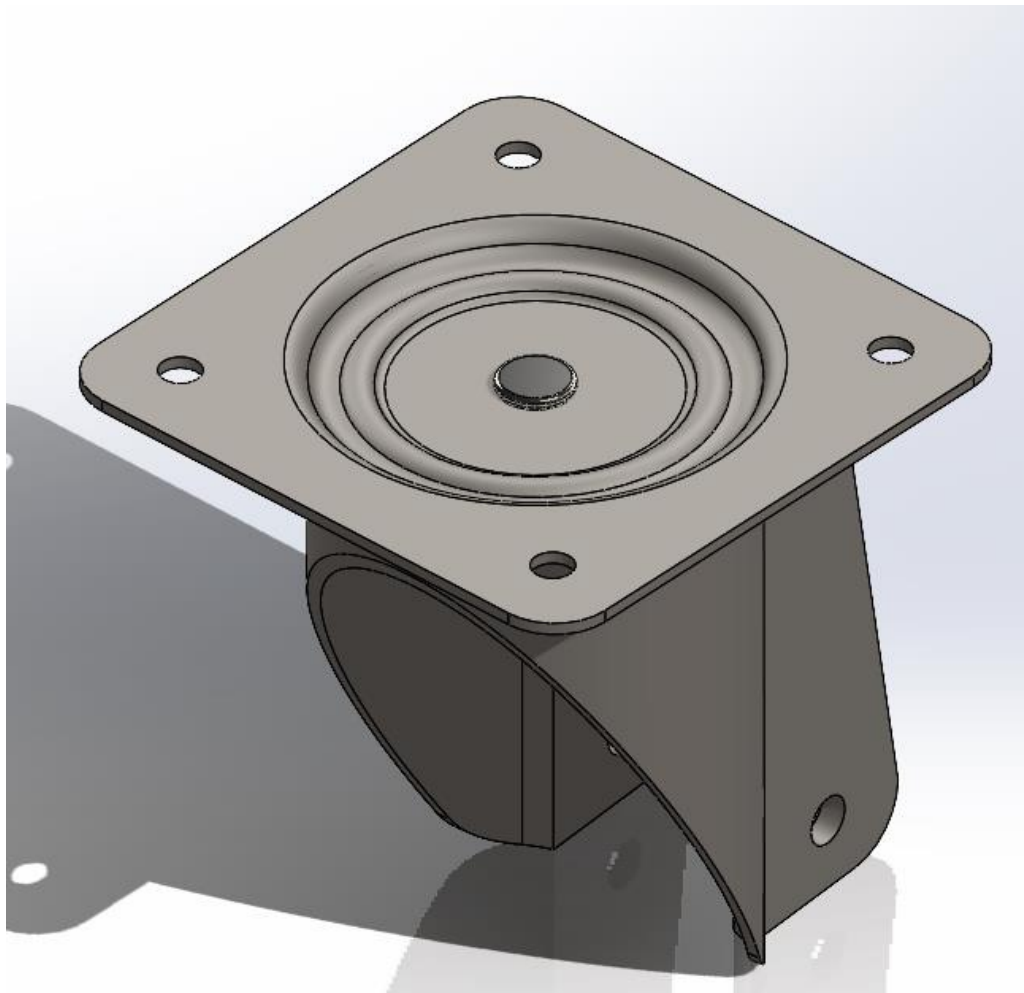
Modelação em ambiente SolidWorks – Estrutura metálica da roda – Vista isométrica
